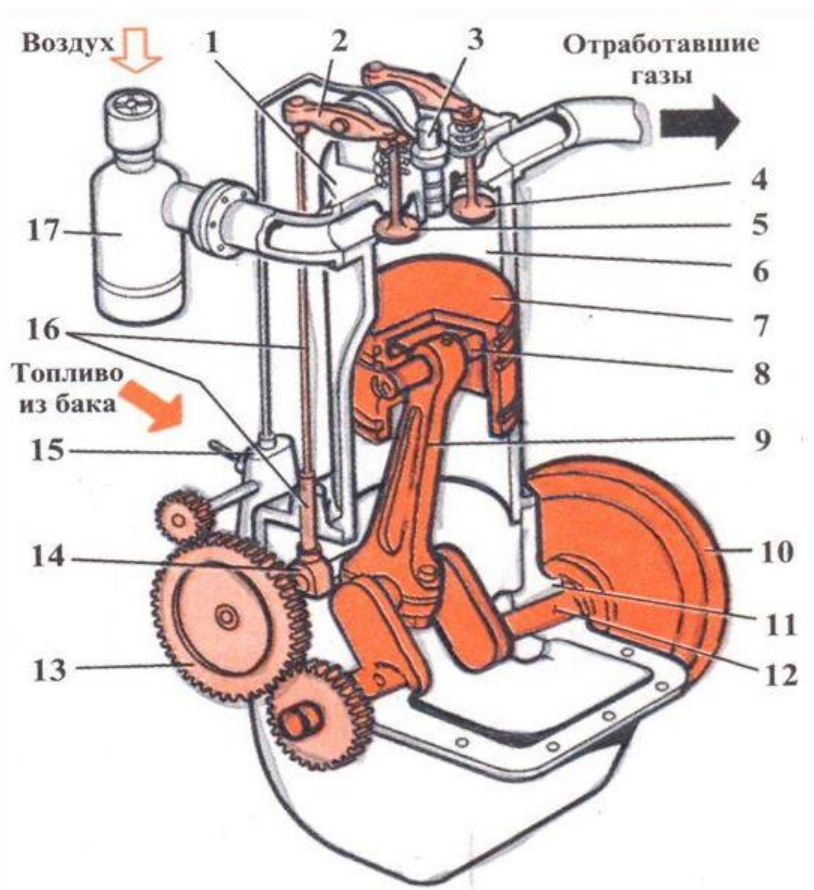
Принцип работы одноцилиндрового дизельного двигателя:
